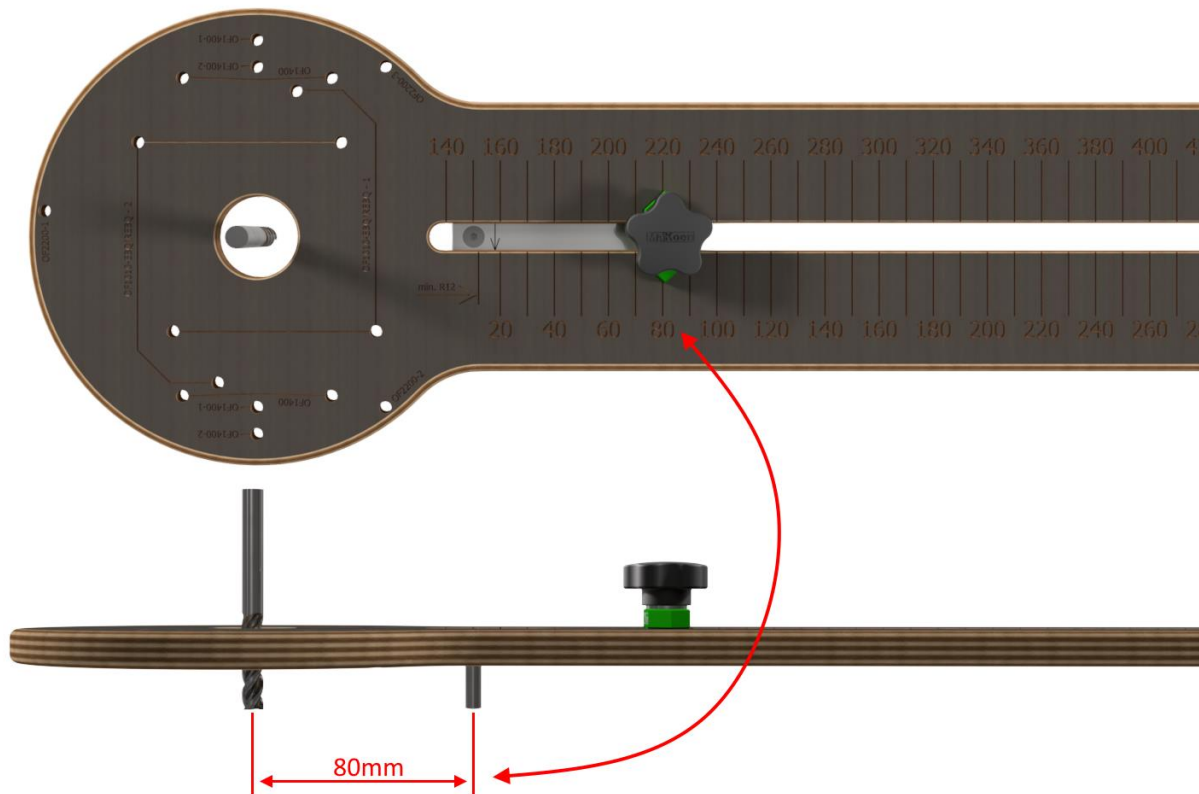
Illustrazione di una dimensione impostata, in questo caso 80 mm
